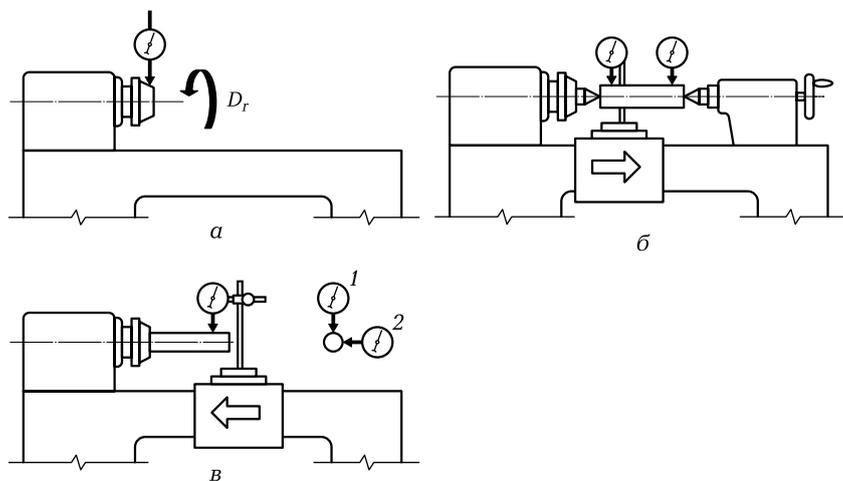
Основные виды проверок токарно-винторезного станка на точность:
